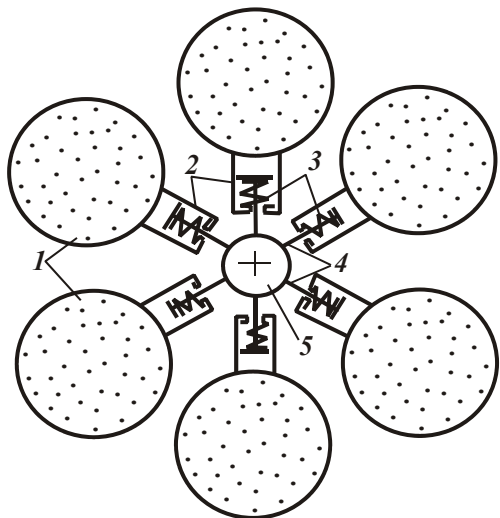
Инструмент для шлифования внутренних поверхностей: 1 – шлифовальный шар; 2 – цилиндр; 3 – пружина; 4 – штырь (спица); 5 – вал.
